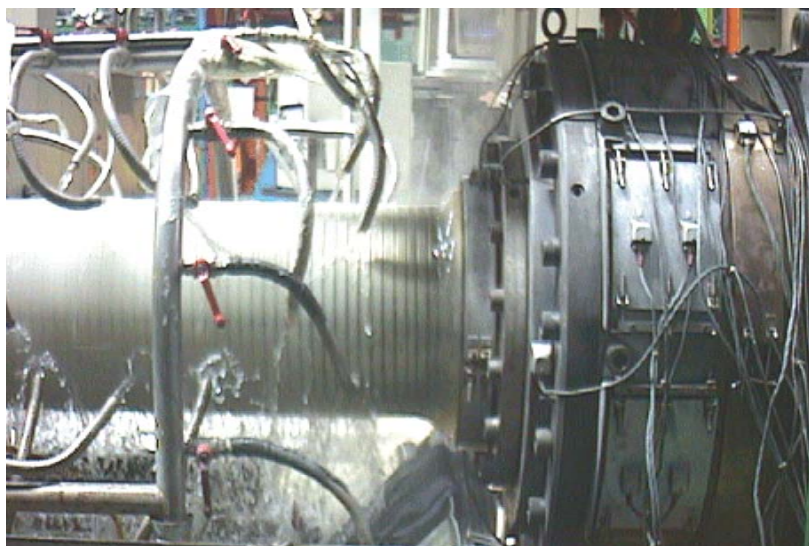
Extrução da barreira de pressão (Petrobras)
